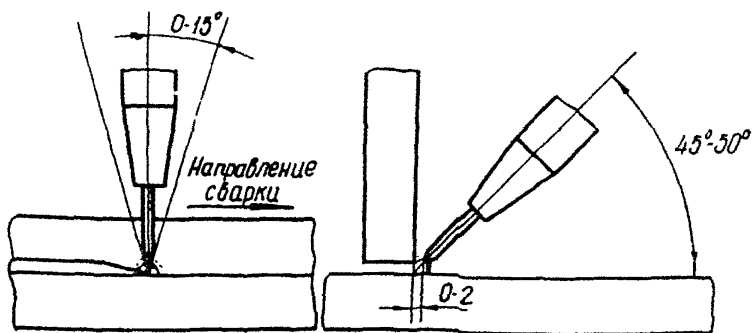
Схема перемещения и угол наклона сварочной проволоки при механизированной сварке угловых и нахлесточных валиковых швов
